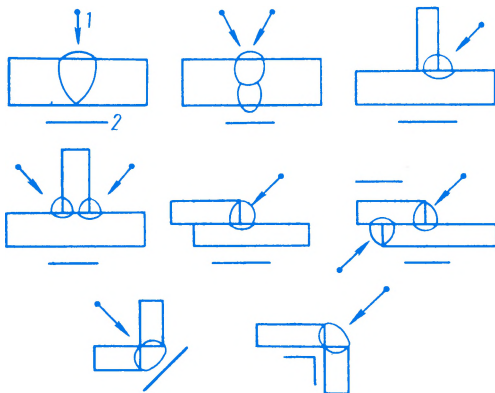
Схема контроля сварных соединений: 1 – направление источника излучения, 2 – рентгенопленка
